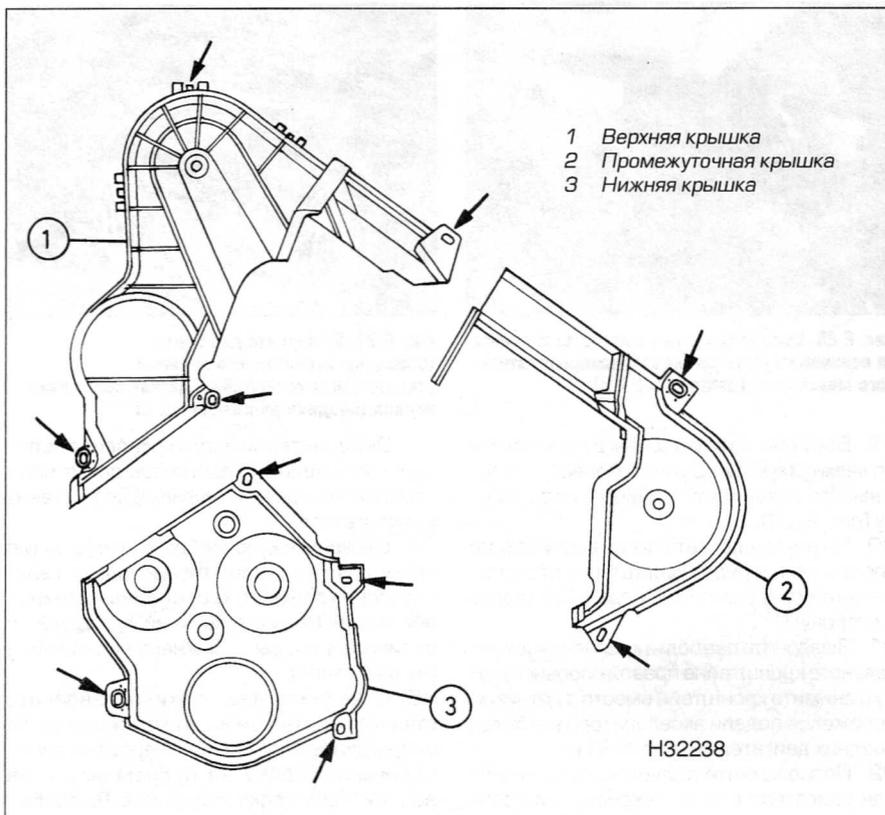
Расположение болтов крепления крышки ремня газораспределительного механизма (отмечены стрелками) (двигатели 1.9 л)
